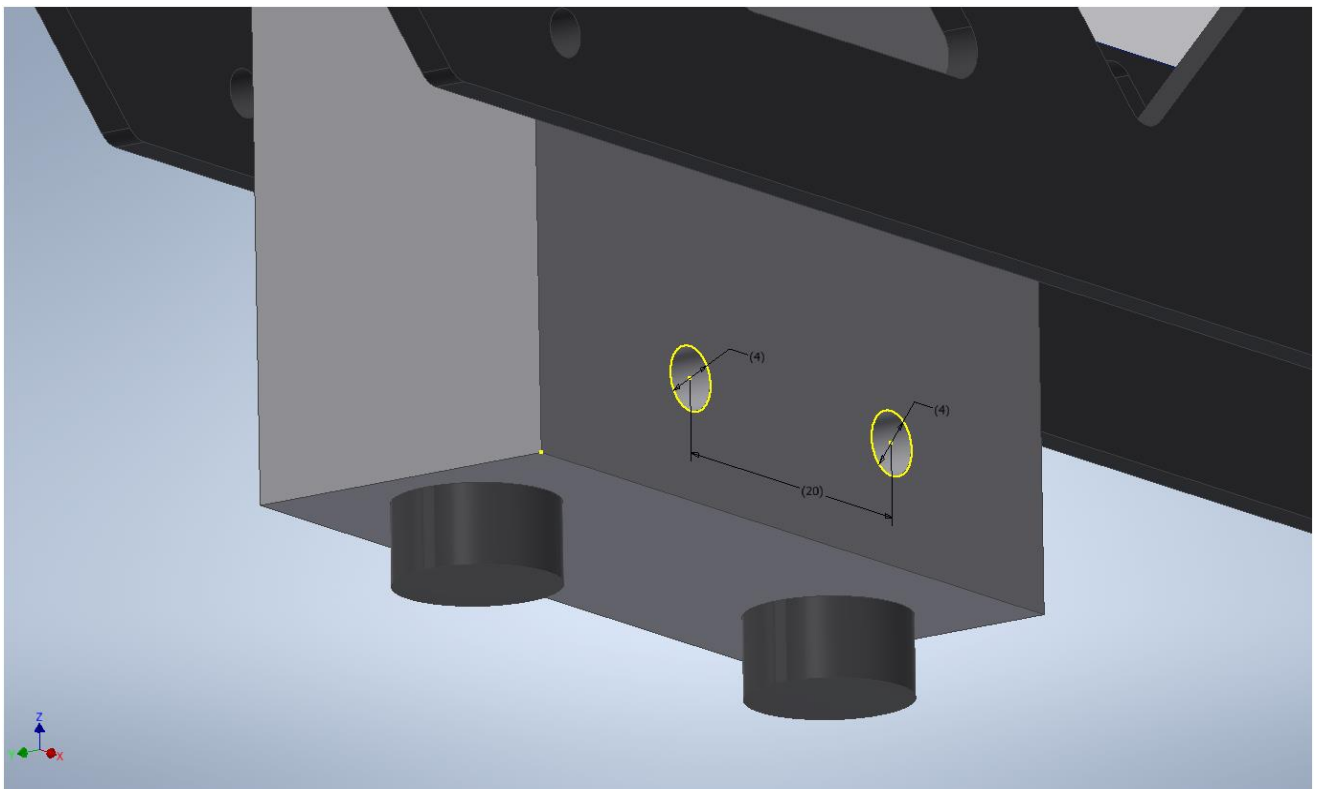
Размеры и расположение отверстий места крепления ПН.
